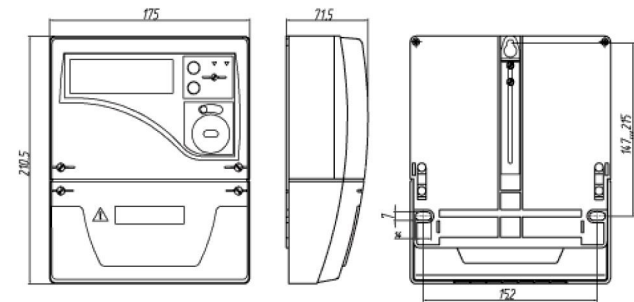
Загальний вигляд лічильника CE303-U в корпусі S31
